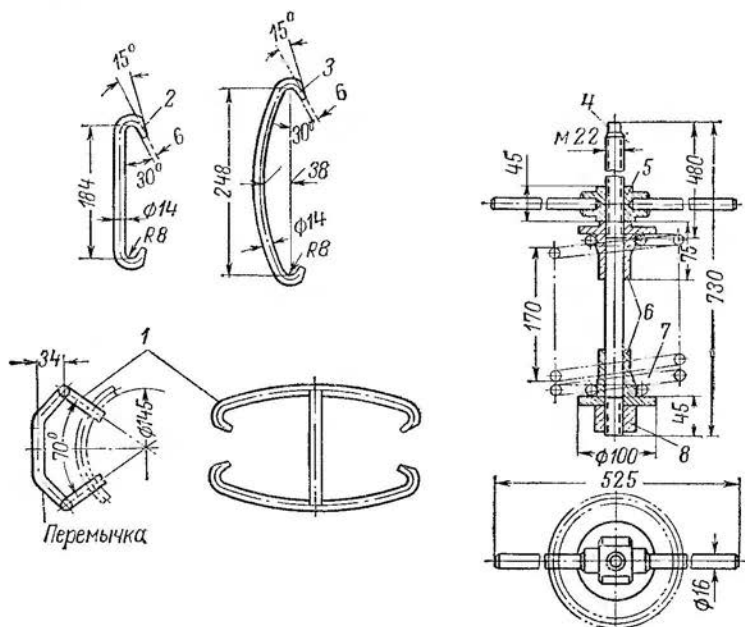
Приспособление для демонтажа и монтажа пружин откидывания;
